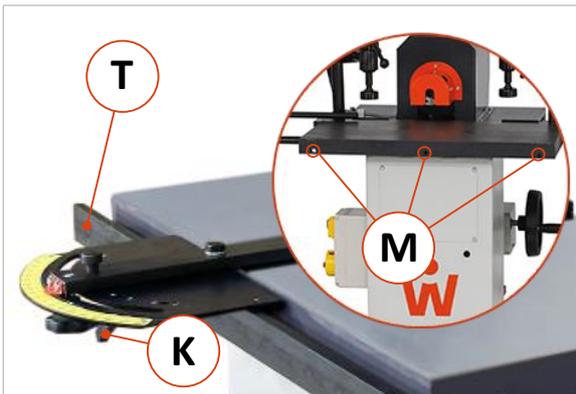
Anbau - Rahmen- und Gehrungsanschlag
